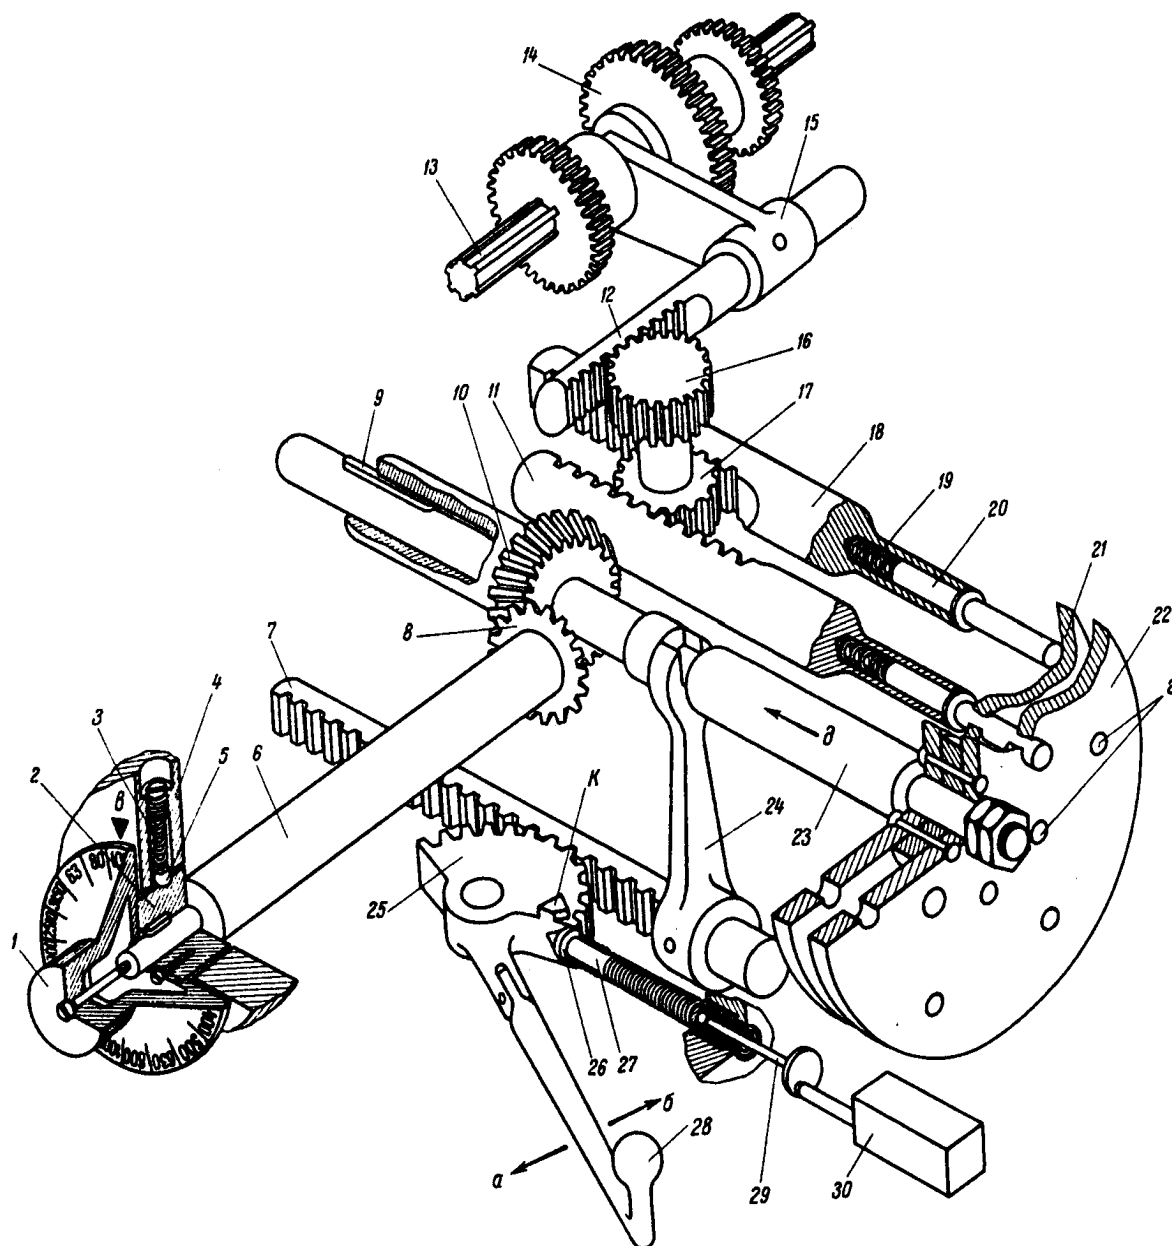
Механизм переключения скоростей вертикально-фрезерного станка мод. 6Н12ПБ:
